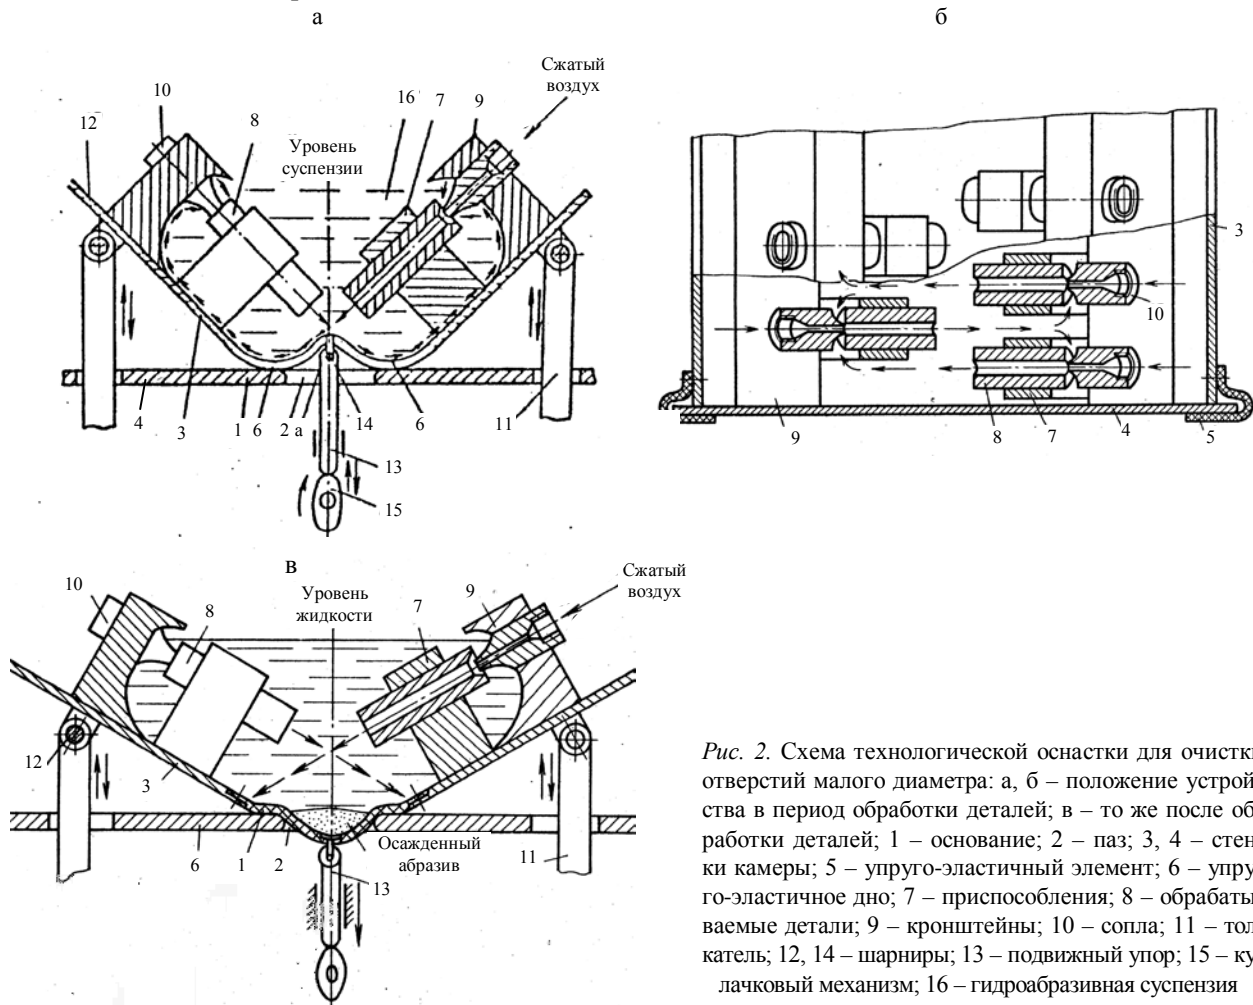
Схема технологической оснастки для очистки отверстий малого диаметра: а, б – положение устройства в период обработки деталей; в – то же после обработки деталей; 1 – основание; 2 – паз; 3, 4 – стенки камеры; 5 – упруго-эластичный элемент; 6 – упруго-эластичное дно; 7 – приспособления; 8 – обрабатываемые детали; 9 – кронштейны; 10 – сопла; 11 – толкатель; 12, 14 – шарниры; 13 – подвижный упор; 15 – кулачковый механизм; 16 – гидроабразивная суспензия
